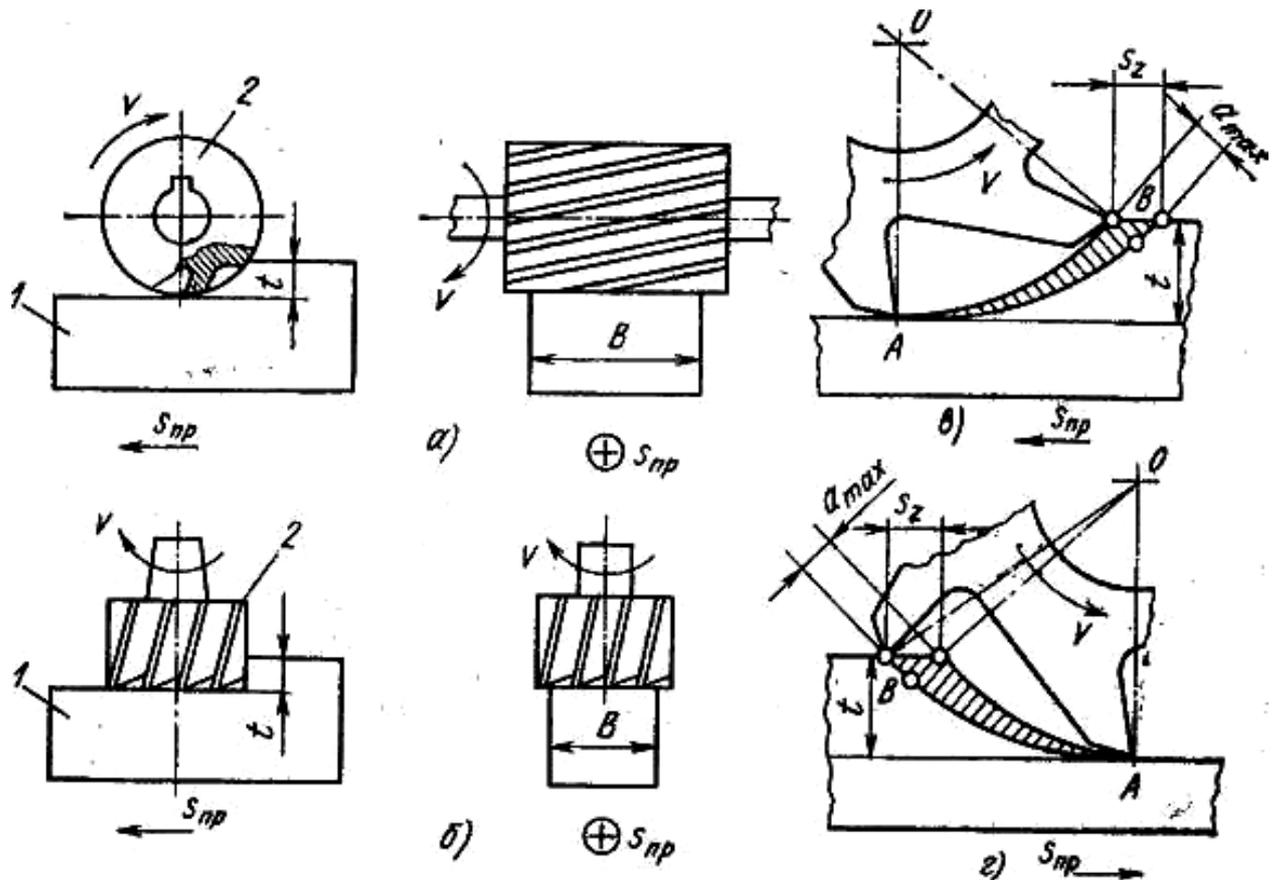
Схемы фрезерования цилиндрической (а) и торцевой (б) фрезами, против подачи (в) и по подаче (г).
